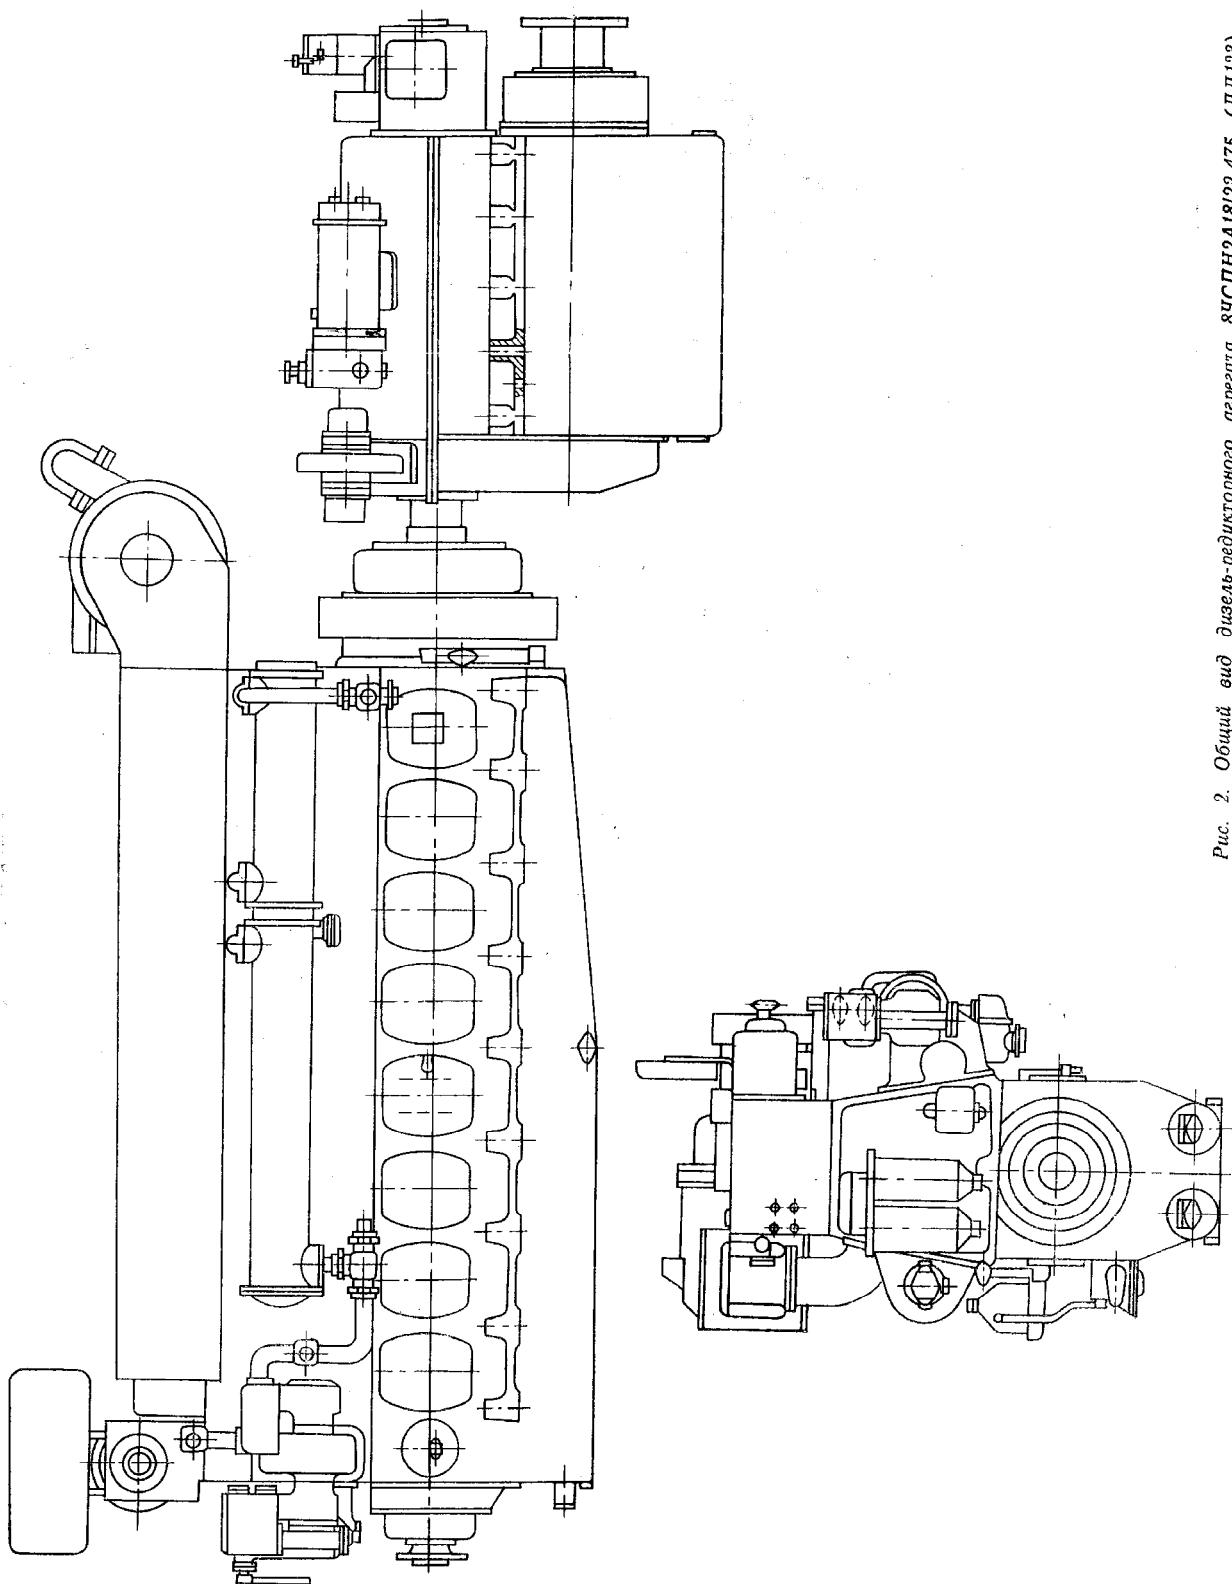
Общий вид дизель-редукторного агрегата 8ЧСПН2А18/22-475 (ДД123)
